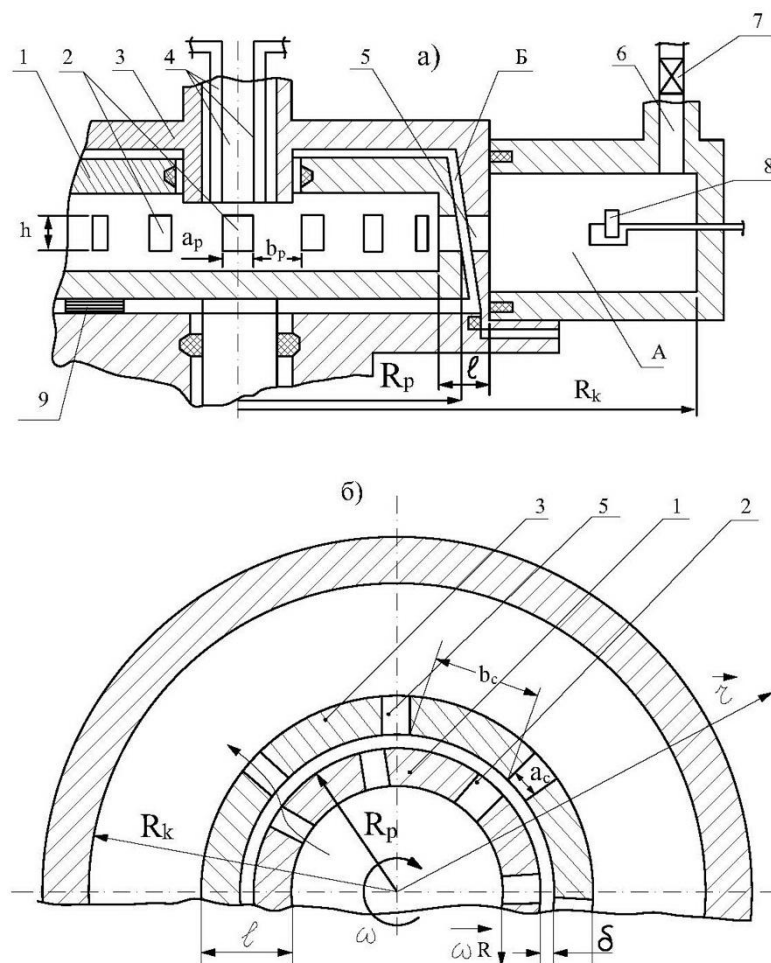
Конструктивная схема роторного гидромеханического диспергатора: а – осевой разрез; б – поперечный разрез: 1 – ротор с патрубками 2; 3 – статор; 4 – три входных патрубка; 5 – патрубки статора; б – выходной патрубков из рабочей камеры А аппарата; Б – зазор между боковыми рабочими поверхностями ротора и статора; 7 – вентиль на выходе аппарата для регулирования давления в рабочей камере А; 8 – датчик акустического давления в камере аппарата; 9 – пластинки Иогансона для регулирования величины зазора δ ; b_p , b_c – ширина промежутка между патрубками ротора и статора на их рабочих поверхностях; a_p , a_c – ширина патрубков ротора и статора в азимутальном направлении; h – высота патрубков ротора; R_p – радиус внешней боковой рабочей поверхности ротора на уровне середины патрубка; R_k – радиус внутренней боковой поверхности камеры; ω – угловая частота вращения ротора; r – радиальная координата
